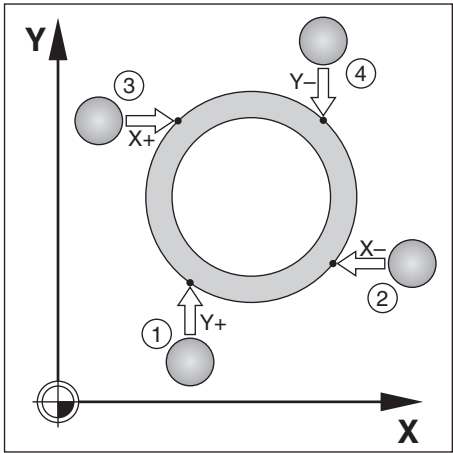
Apalpação da parede exterior do círculo para cálculo da posição do ponto central
